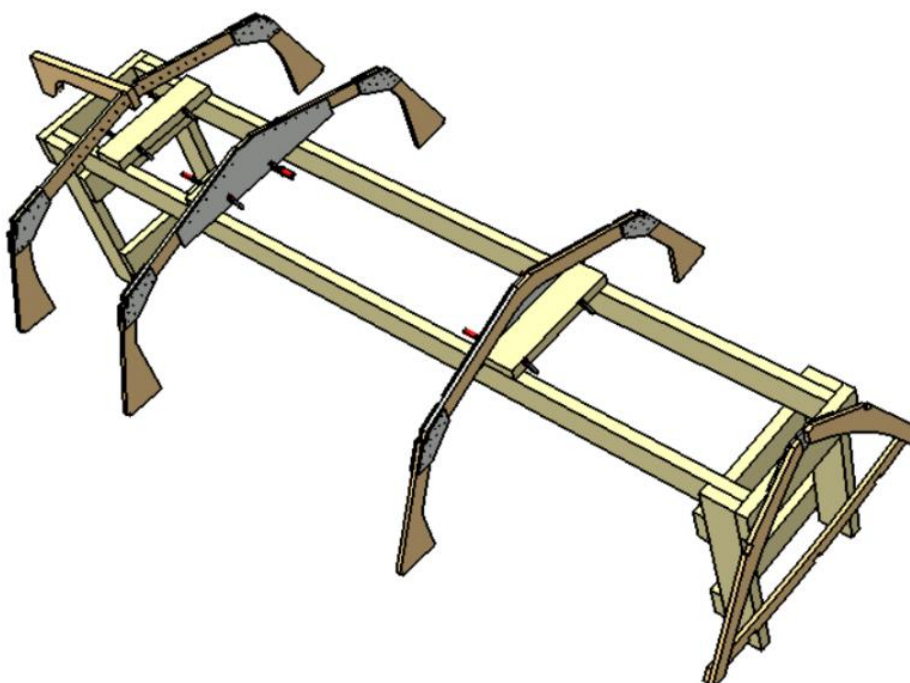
Colocación cuaderna en banco de construcción. Fuente: propia
